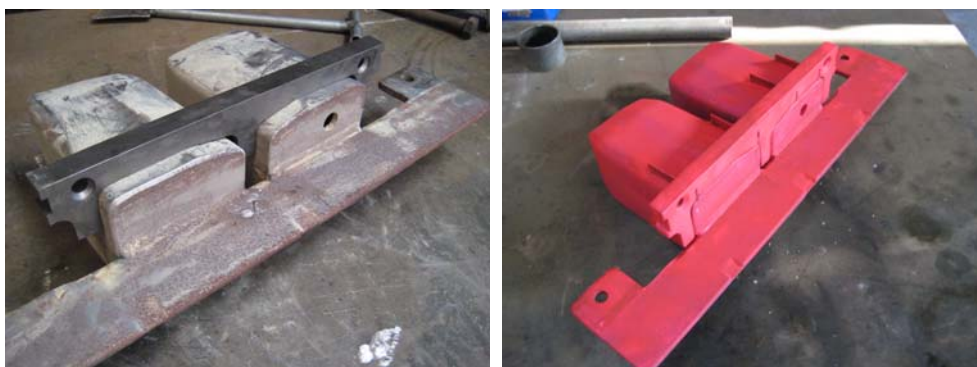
Montaje de puente con corazones y zapata estándar [izquierda]. Montaje de puente con corazones y zapata modificados [derecha].
